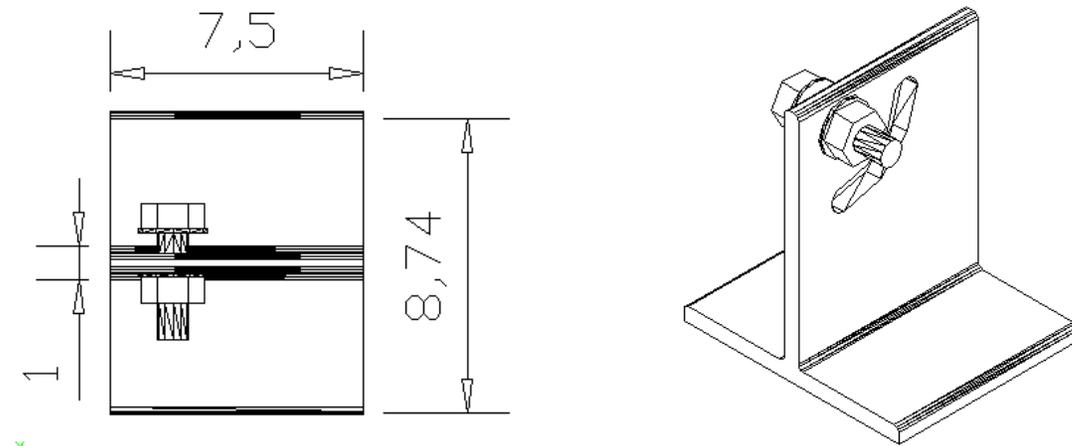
Vista y Dibujo de conjunto de Pieza que sujeta el otro extremo del alternador
